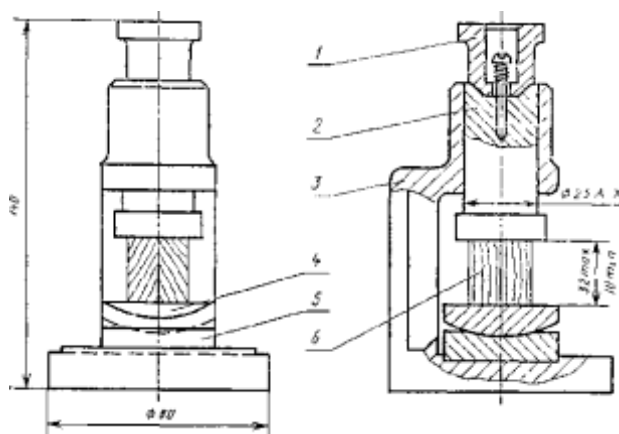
Приспособление к испытательной машине. 1– колпачок; 2 – пуансон; 3 – корпус; 4 – шаровая опора; 5 – плита; 6 – образец.
